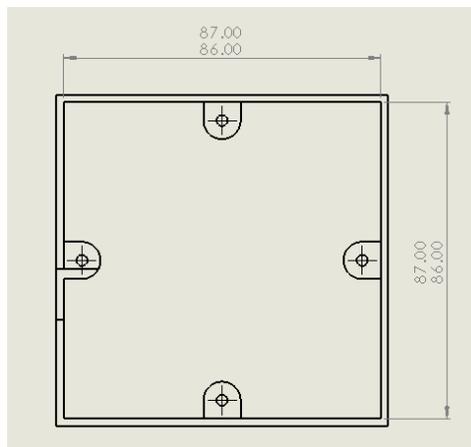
Imagen de aumento de dimensiones para tolerancias
